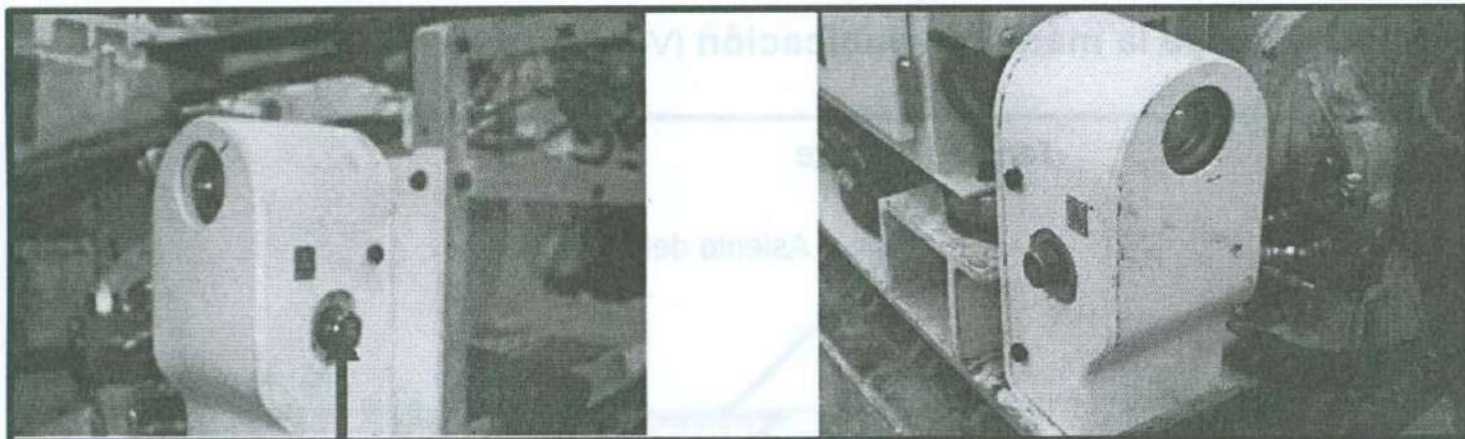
C. Parte frontal izquierda y parte frontal derecha.
